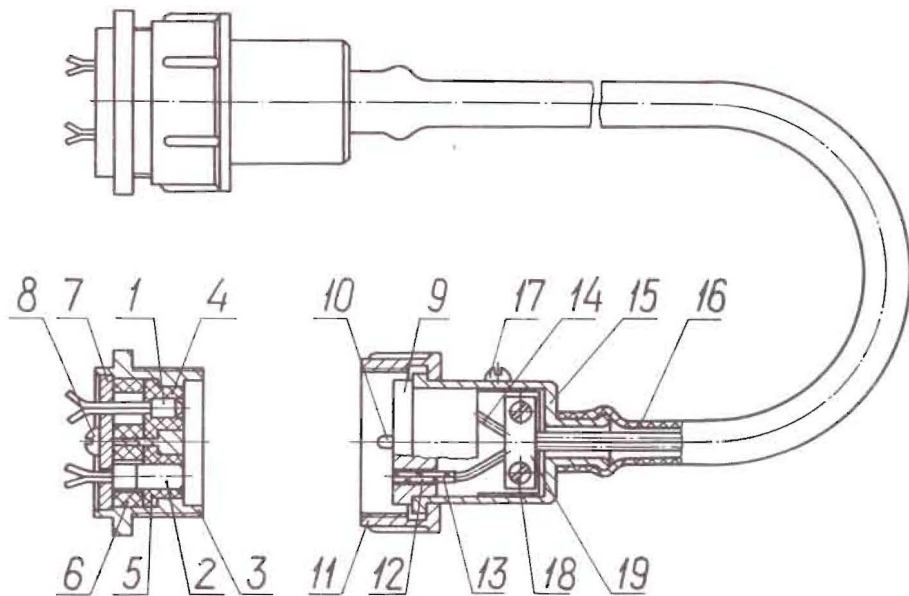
Бинарный оптический соединитель: 1 - светодиод; 2 - фотодиод; 3 - приборный корпус соединителя; 4,5 - изолирующая втулка; 6 - изолирующая шайба; 7 - фиксирующая шайба; 8,17,18 - винт; 9 - контактная втулка; 10 - штифт /фиксатор/; 11 - гайка накидная; 12 - капилляр; 13,14 - световод; 15 - защитный кожух; 16 - резиновый наконечник; 18 - прижимная пластина.
